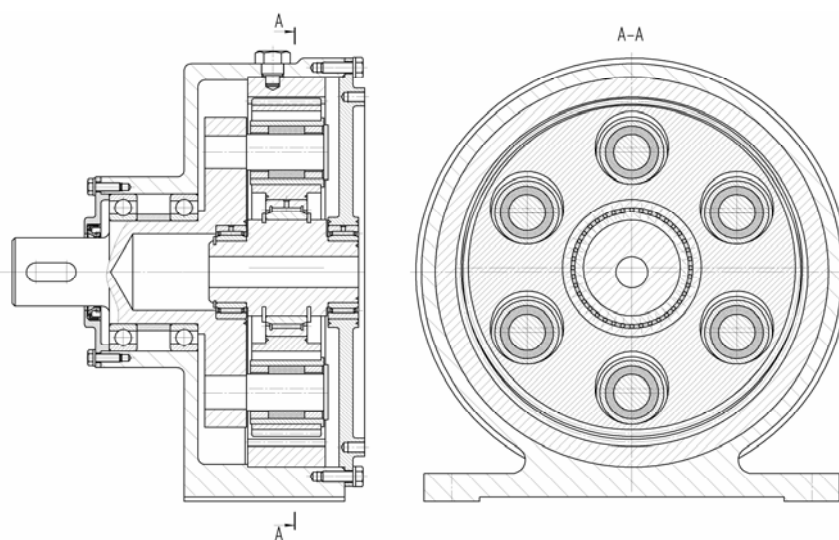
Планетарная передача с внутренним зацеплением колес и цевочным механизмом снятия движения с сателлита
